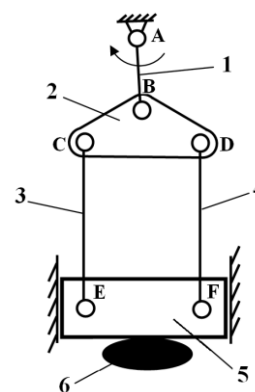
Кинематическая схема нового кривошипного пресса на базе плоского рычажного механизма 4-го класса
